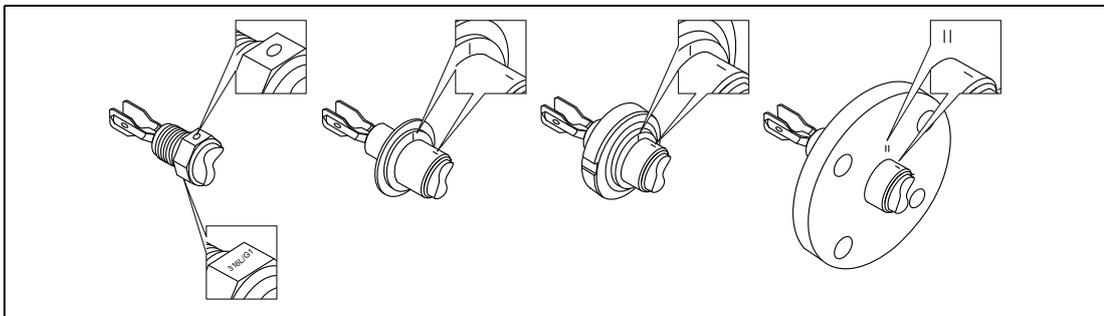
Markierungen für die Ausrichtung der Schwinggabel
